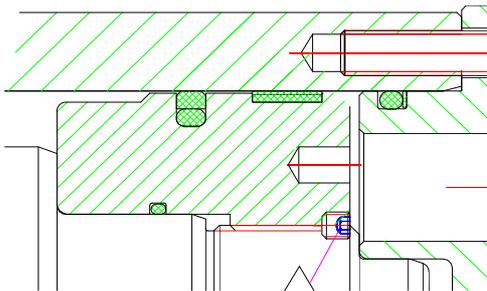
Kolben mit Glydring/Wynseal- Dichtung
